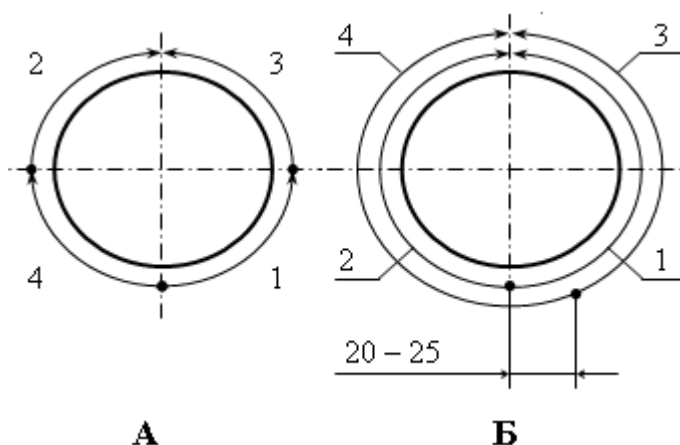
Порядок сварки неповоротного кольцевого стыка одним сварщиком: А – корневой слой шва вертикального стыка; Б – второй и последующие слои шва вертикального стыка; 1; 2; 3; 4 – последовательность выполнения участков и слоев (РД-25.160.00-КТН-011-10)
